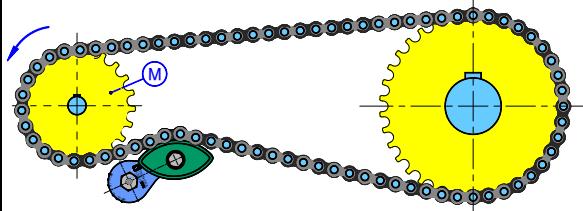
Montaggio corretto con azionamento dall'esterno.
